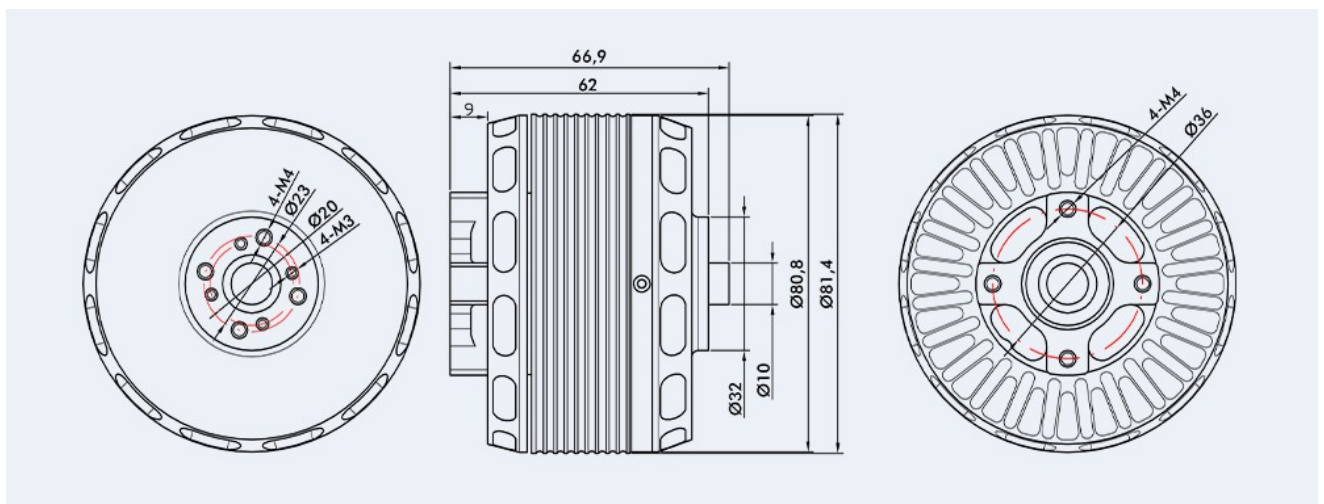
Кресленики двигуна T-Motor AT7224
